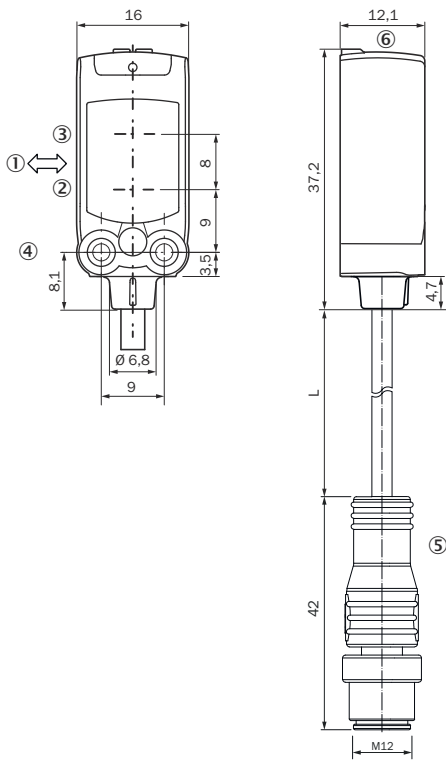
Disegno dimensionale 1, cavo con connettore maschio M12
